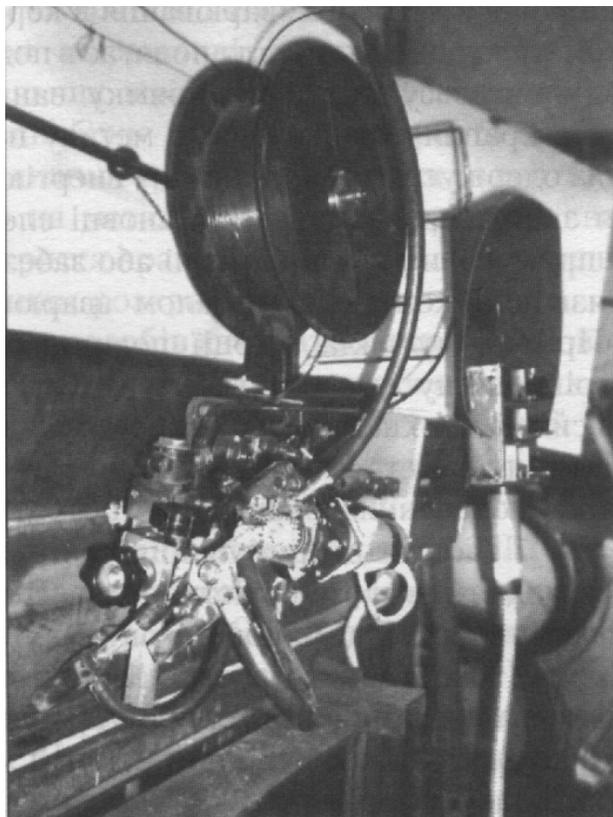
Образец монтажного аппарата для сварки уторных швов ток вертикальной стены (практически на всю высоту резервуара) по периметру корпуса равнялся почти 25 %. В условиях ремонта резервуара использовали два процесса автоматизированной дуговой сварки: под флюсом – для соединения отдельных листов в монтажные блоки и самозащитной порошковой проволокой – для стыковых горизонтальных швов на вертикальной плоскости при монтаже блоков на вертикальной стенке. При сварке под флюсом в нижнем положении швов для толщины металла 9,0-12 мм применяли электродную проволоку Св-08ГА диаметром 5 мм и флюс АН-60СМ. Сварку выполняли трактором АДФ-1002 с источником питания ВДУ-1201 на режиме: $I_{св} = 720-850$ А, $U_{д} = 30-38$ В, $V_{св} = 20-28$ м/ч. Качественного формирования обратной стороны швов достигали с помощью флюсомедной подкладки. Для замены стенки резервуара необходимо было сварить шесть отдельных блоков в специальном кондукторе (рис. 2).
